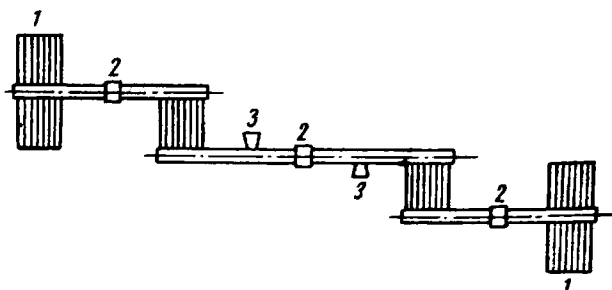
Схема агрегата для огневой зачистки полупродукта:
